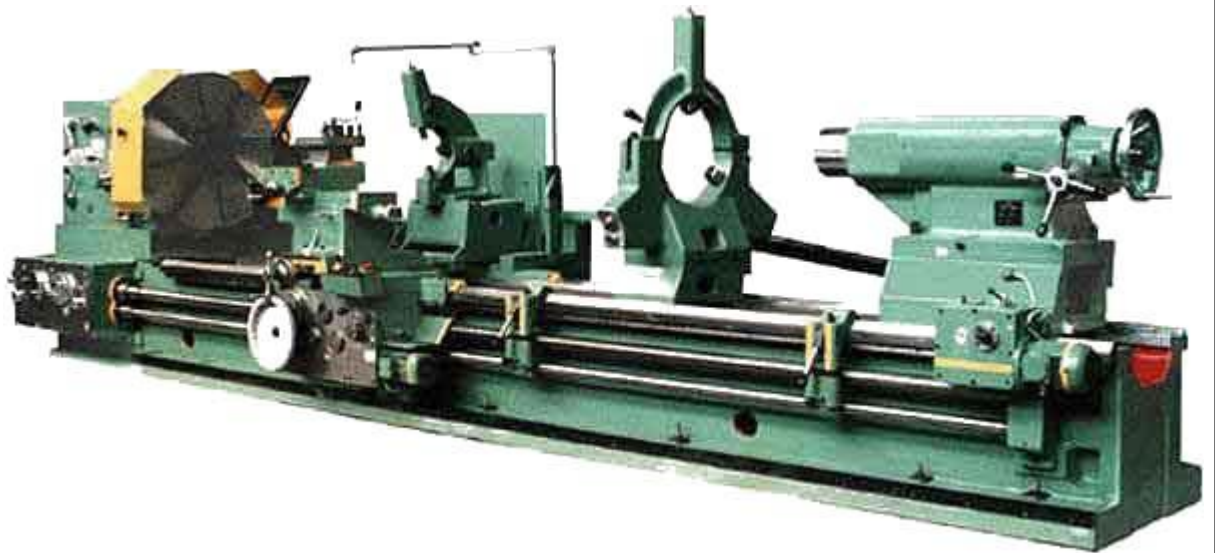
Верстат токарно-гвинторізний 1М63
